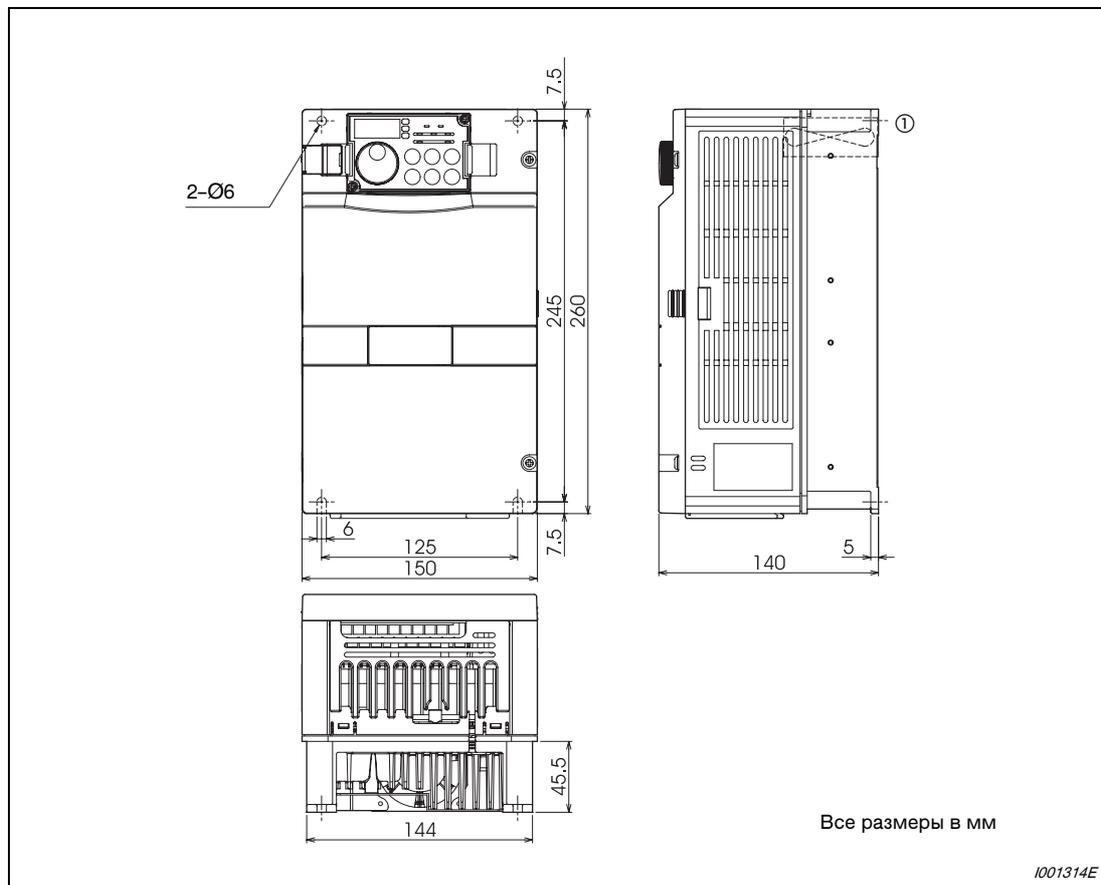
Размеры FR-A 740-00023 ... -00126
